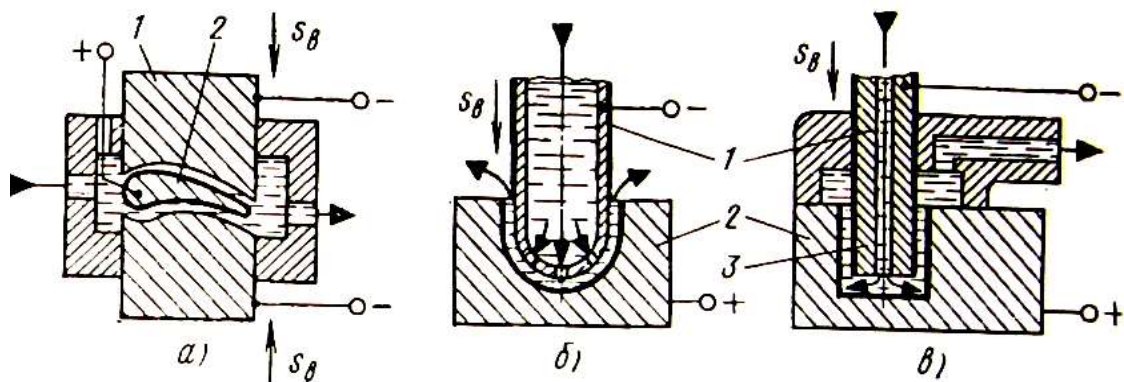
Схема електрохімічної розмірної обробки:
